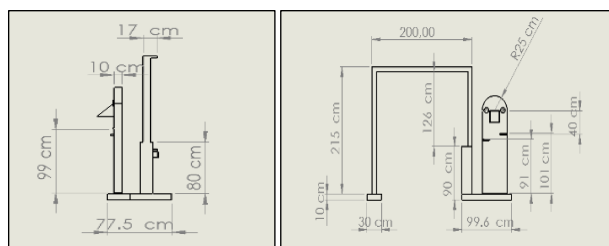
Planos Pieza 1: estructura o Armazón. Fuente:
